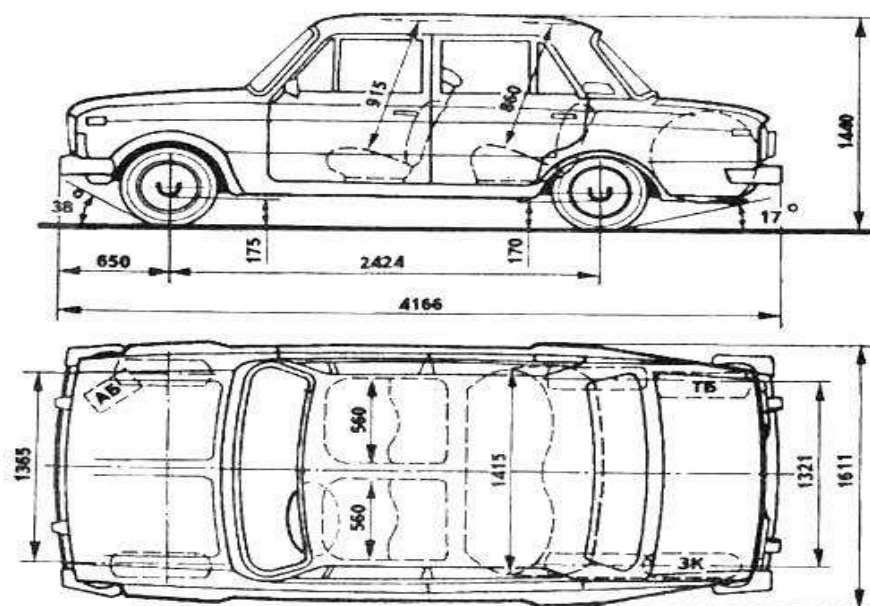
Габаритні розміри автомобіля ВАЗ-2106
